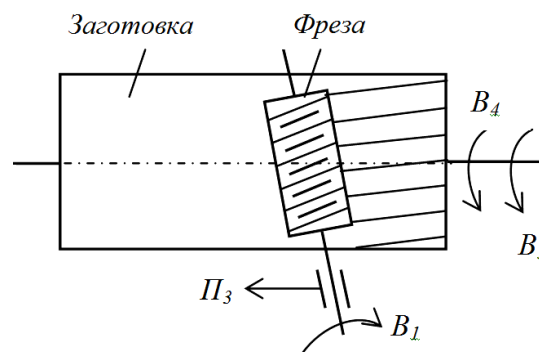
Способ фрезерования червячной фрезой шлицевых валов и вал-шестерен
